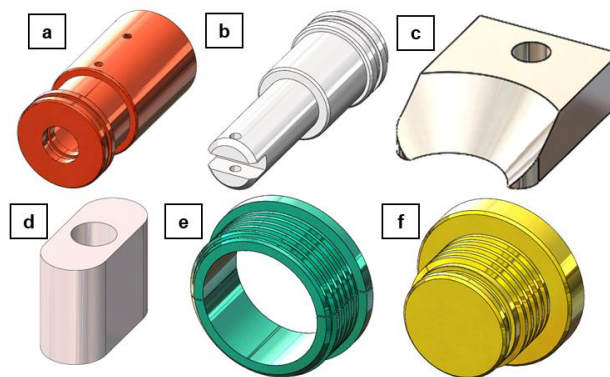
Componentes del cortador de cable de registro. a) Cuerpo hidráulico, b) Embolo, c) Cuchilla de corte, d) Cuña para émbolo, e) Tuerca bipartida, f) Tapón de cuerpo hidráulico.
